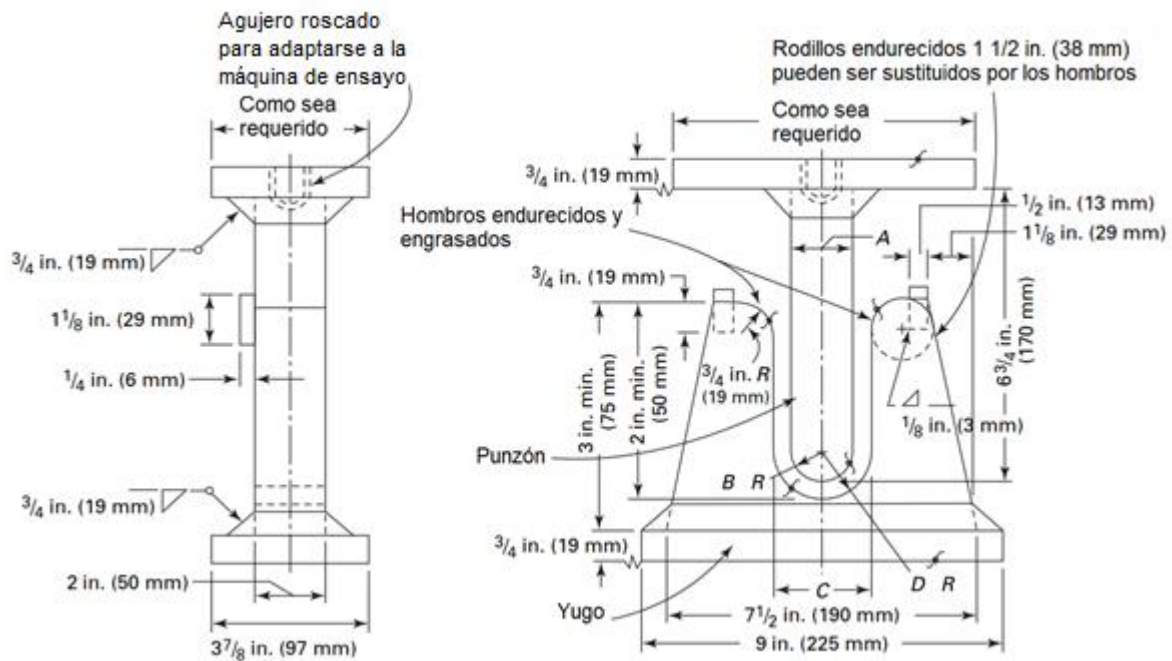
Dimensiones de plantilla para prueba de doblado (QW-466.1)
